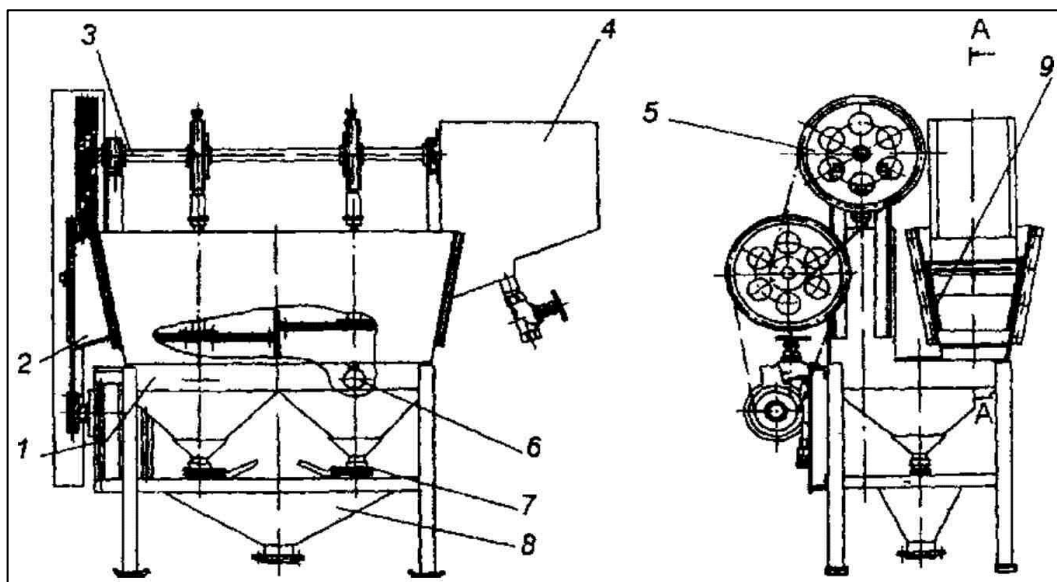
Схема машины отсадочной поршневой МОП-0,2: 1 - корпус; 2 - лоток; 3 - кривошипно-поршневой механизм; 4 - бункер; 5 - привод; 6 - обратный клапан; 7 - затвор; 8 - воронка; 9 - решетная камера
